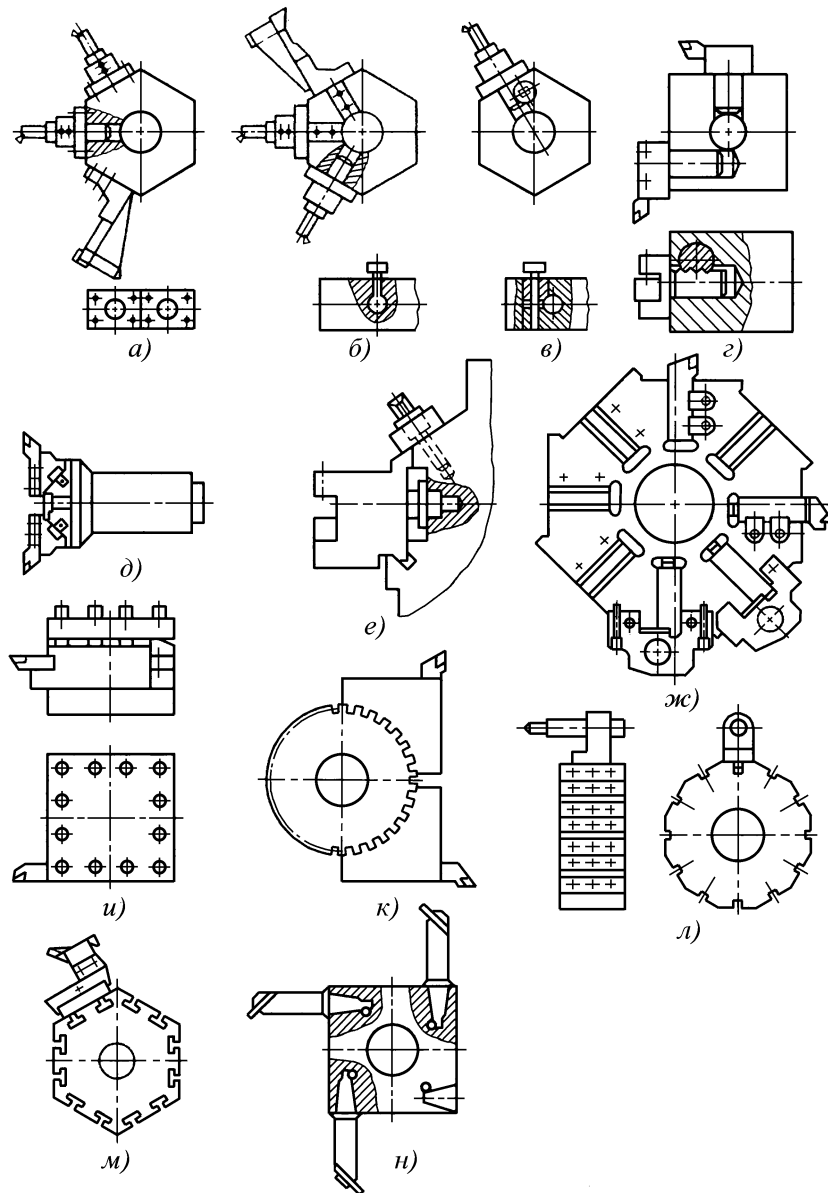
Способы крепления инструмента на токарных станках с ЧПУ
